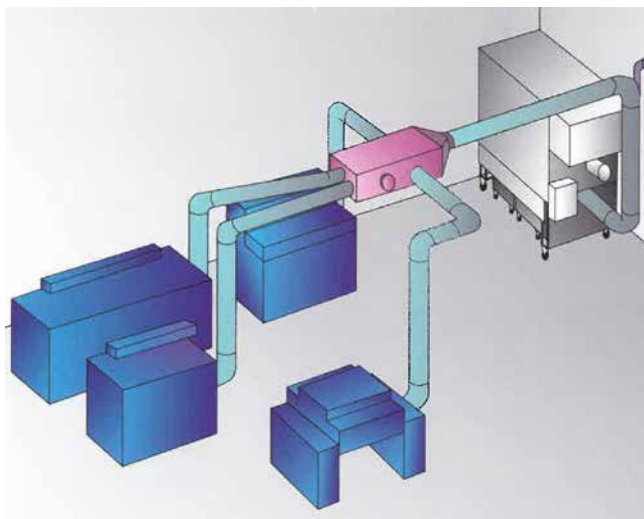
+ b Aufbau eines Klappenkastens zum Anschluss mehrerer Maschinen(-Gruppen) bei gleichzeitiger Sicherstellung ausreichender Transportluft
